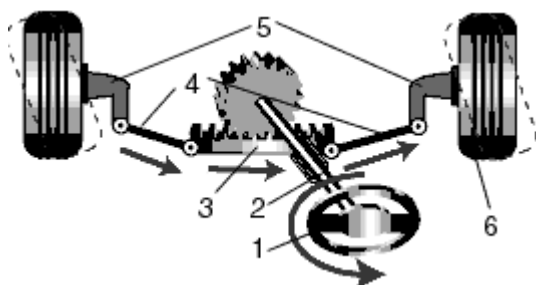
Схема рулевого управления с механизмом типа «шестерня-рейка» 1 - рулевое колесо; 2 - вал с приводной шестерней; 3 - рейка рулевого механизма; 4 - правая и левая рулевые тяги; 5 - поворотные рычаги; 6 - направляющие колеса
